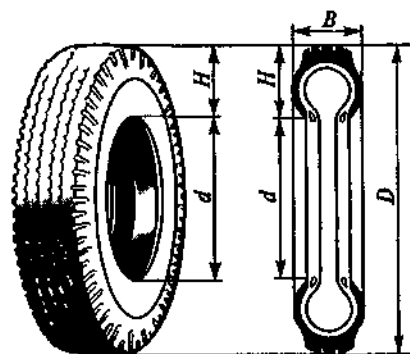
Основные размеры шин: B и H — ширина и высота профиля; d и D — посадочный и наружный диаметры
